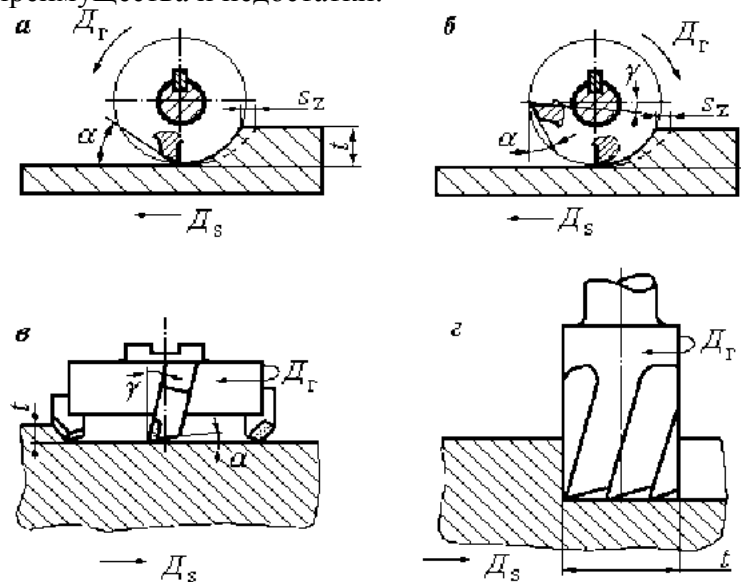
Виды фрезерования: а – против подачи; б – по подаче; в – торцовой фрезой; г – концевой фрезой
